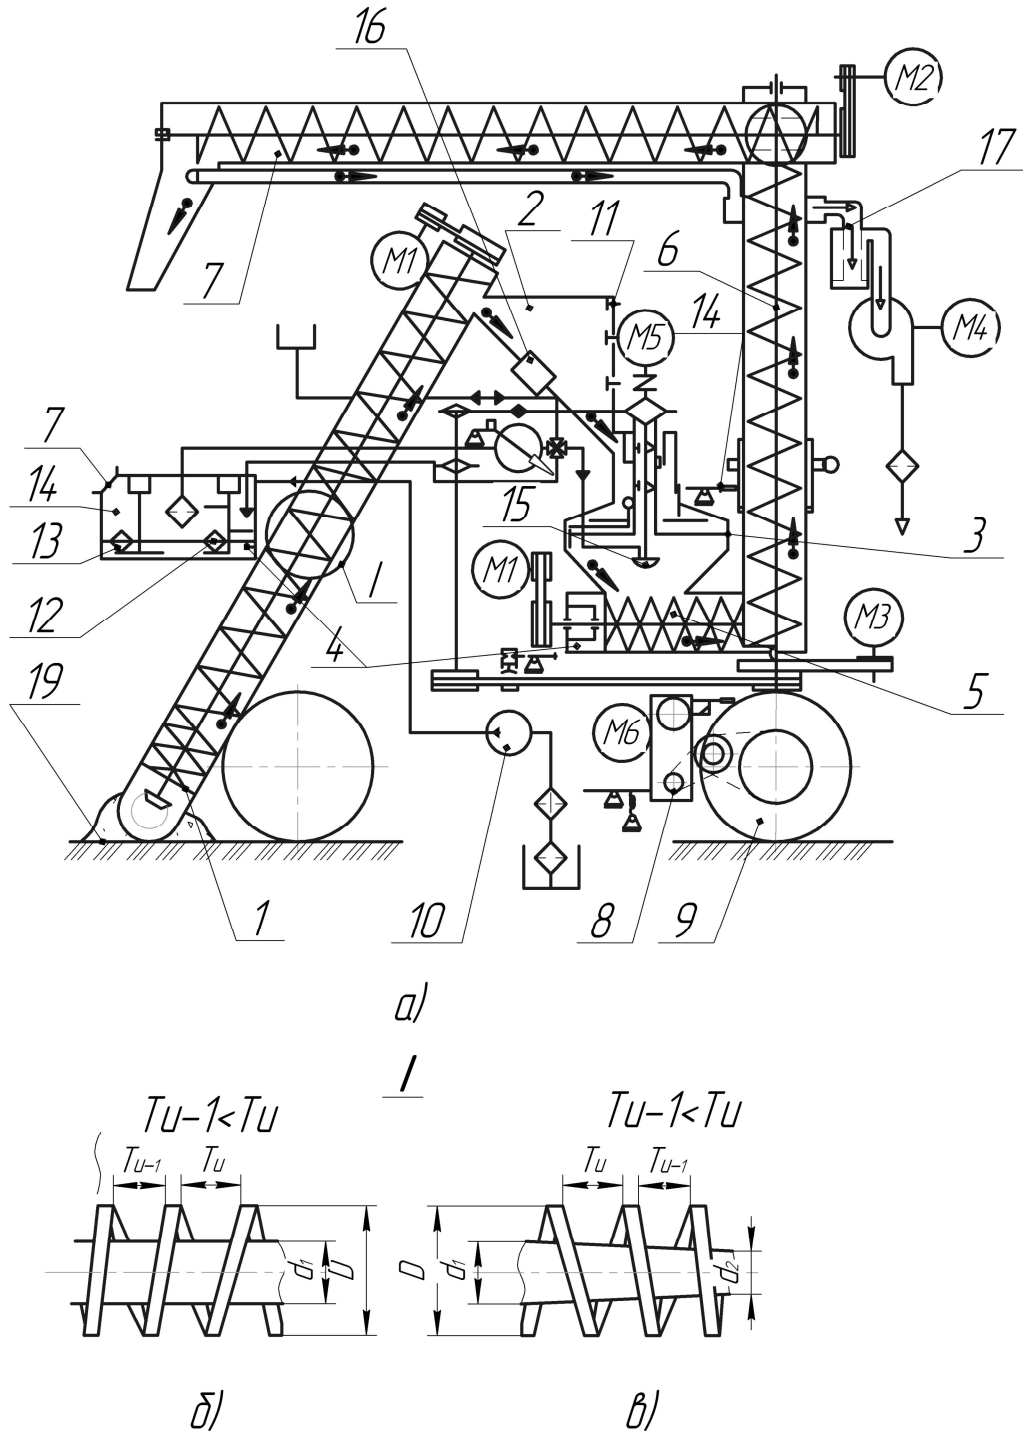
а) Енергоощадний протруювач насіння; б) гвинтові робочі органи циліндричної форми зі змінними кроками; в) гвинтові робочі органи циліндричної форми з конічними валами
